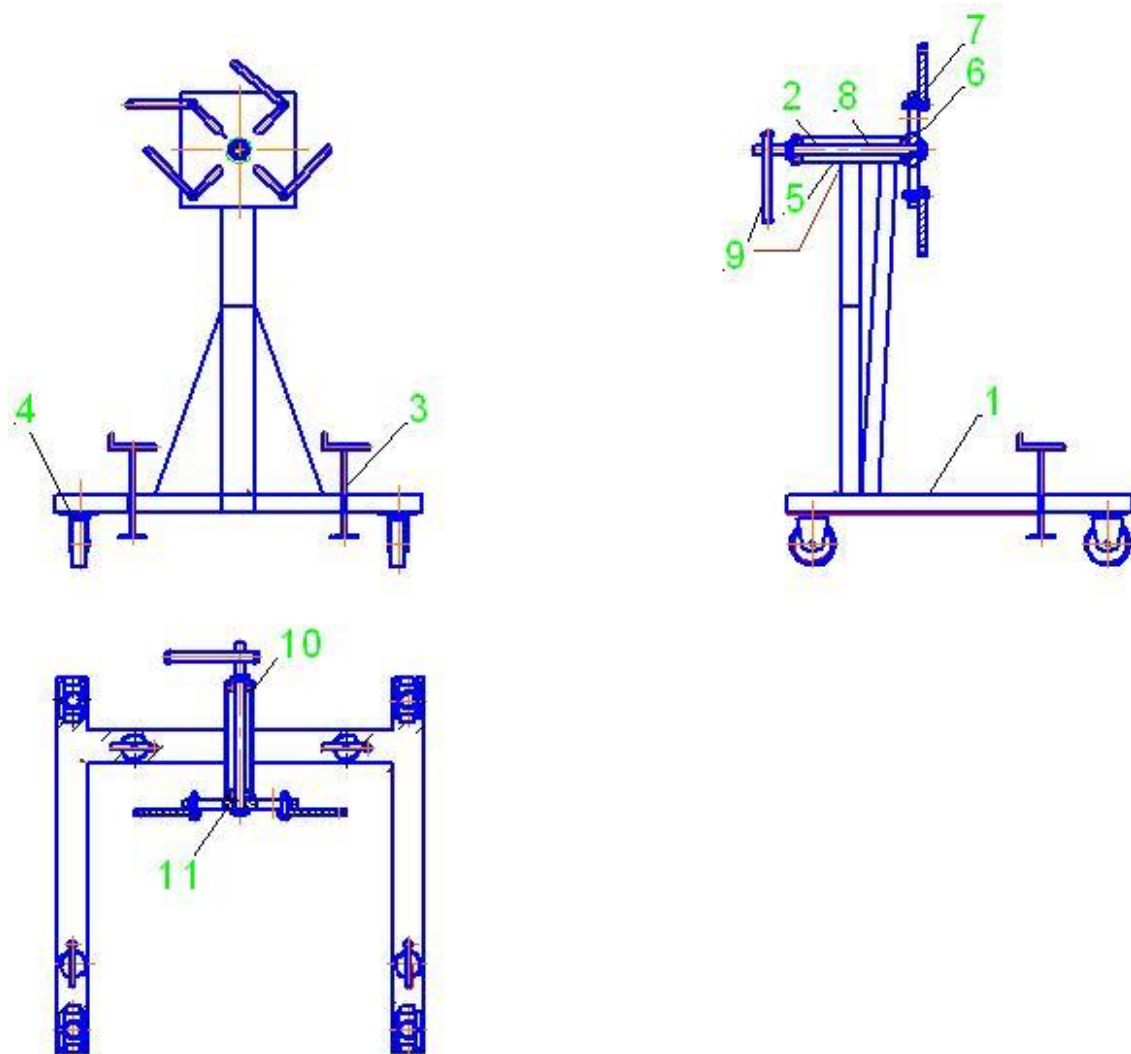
Стенд для розбирання головки блока циліндрів.
